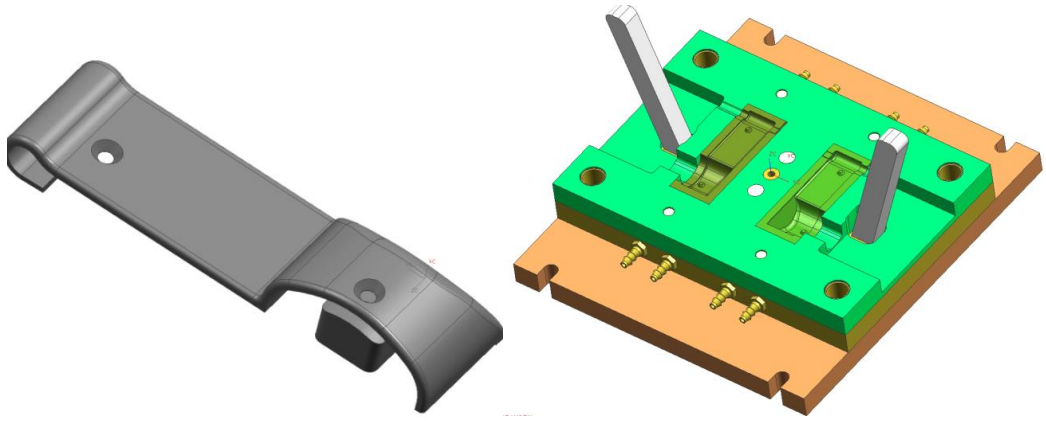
Деталь кассового аппарата и пресс-форма для её изготовления
